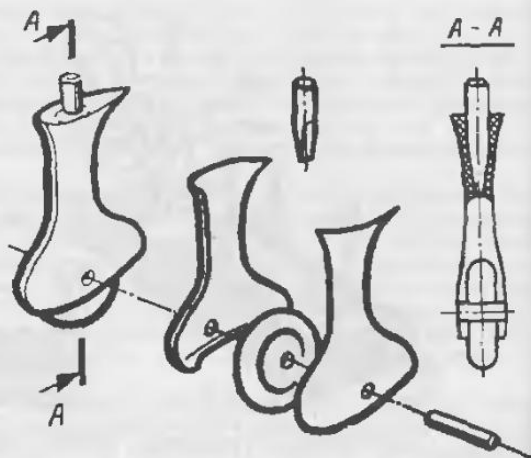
Изготовление стойки с обтекателями колес, полученной штамповкой в свинец
